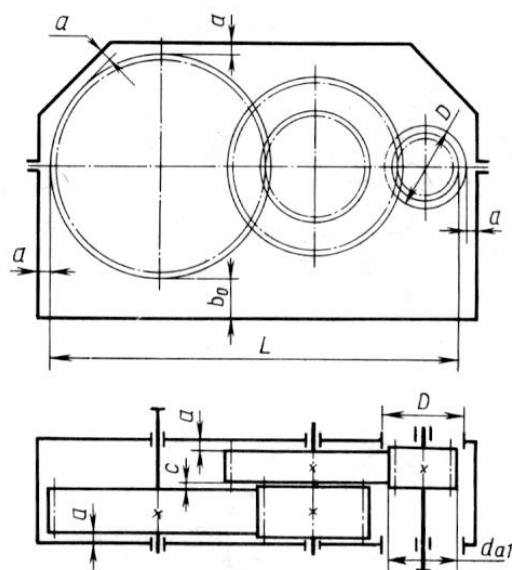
Редуктор цилиндрический двухступенчатый по развернутой схеме
